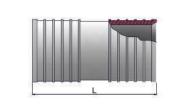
Пресс-муфта соединительная равнопроходная Тип 1 для труб типоразмеров 50 и более
